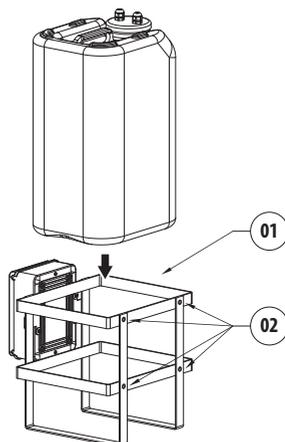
Réservoir 23l, hauteur de remontée de 5m ou 11m.
